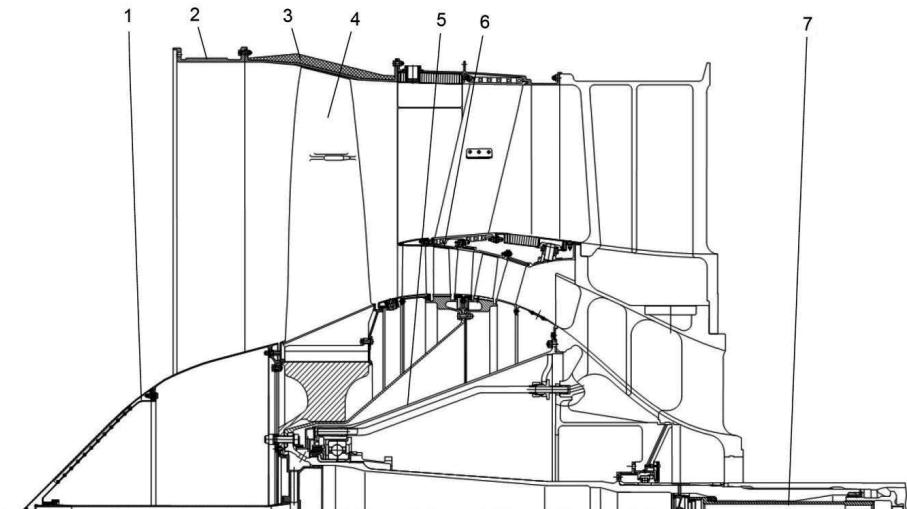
Схема основных узлов вентилятора двигателя ПС-90А:
